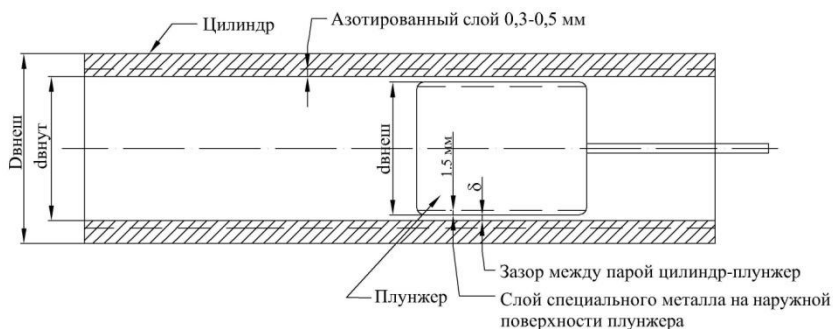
Конструктивные размеры пары цилиндр-плунжер
